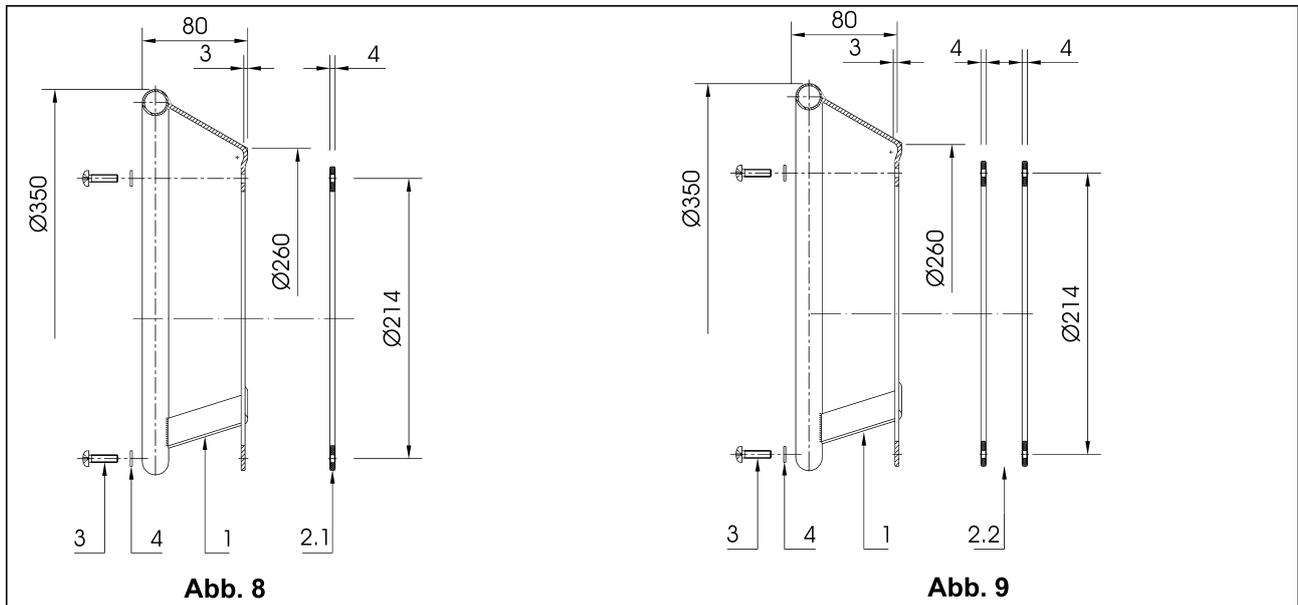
Haltegriff für Betonbecken Art. Nr. E30040130
